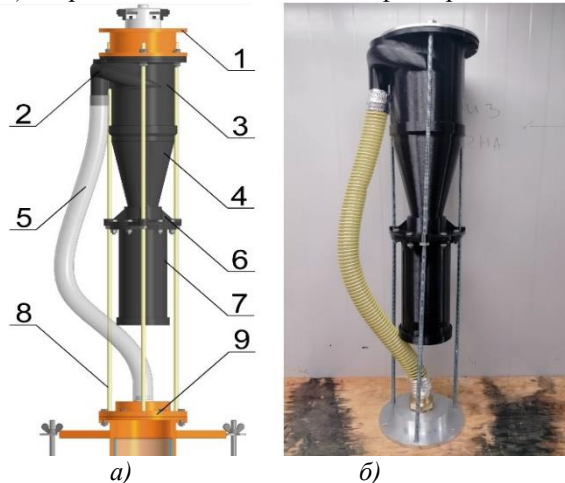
а) – конструкция циклонного фильтра №1: 1 – верхний фланец; 2 – входной патрубок; 3 – цилиндрическая часть; 4 – конусная часть; 5 – шламоподъемный шланг; 6 – переходник; 7 – шламосборный бак; 8 – шпильки; 9 – нижний фланец, б) – общий вид циклонного фильтра №1
